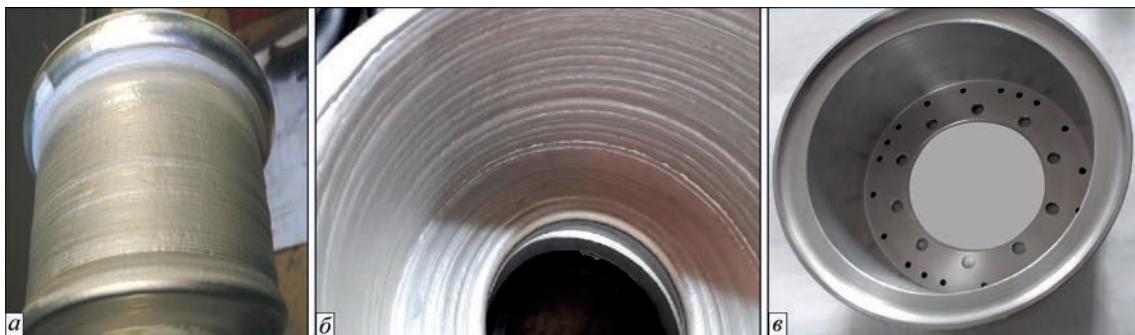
Диск автомобільного колеса з алюмінієво-магнієвого сплаву 1580, виготовлений АПДН на постійному струмі зворотної полярності [17]: вигляд зовнішньої поверхні (*a*) і внутрішньої порожнини (*б*) після 3D друку; вигляд після механічної обробки (*в*)
